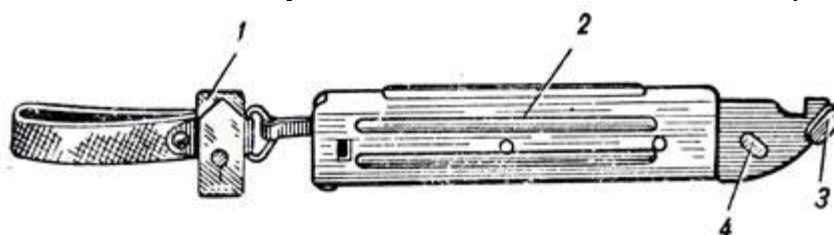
Ножны: 1 - подвеска с карабинчиками; 2 - пластмассовый корпус; 3 - упор; 4 - выступ-ось
